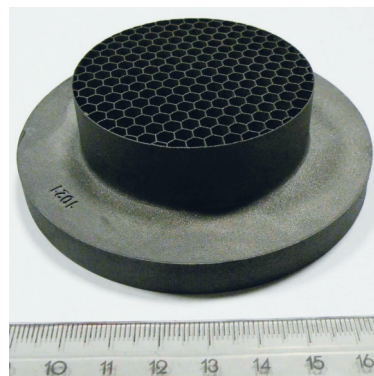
Люминесцентный контроль детали «Пламегаситель»
